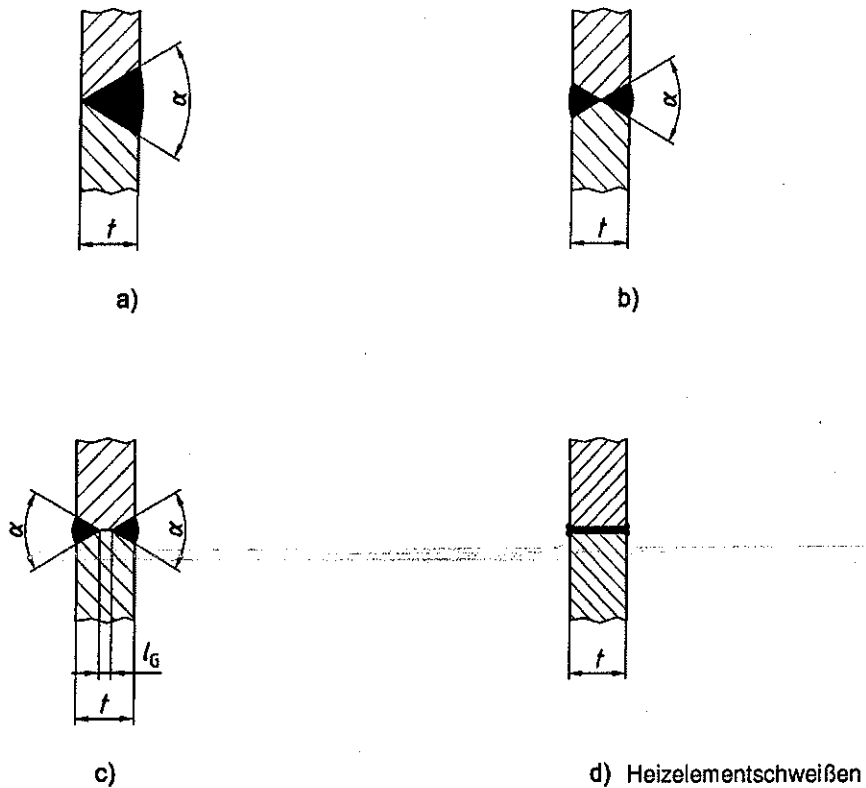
Schweißverbindung zwischen Tankwand und Boden
